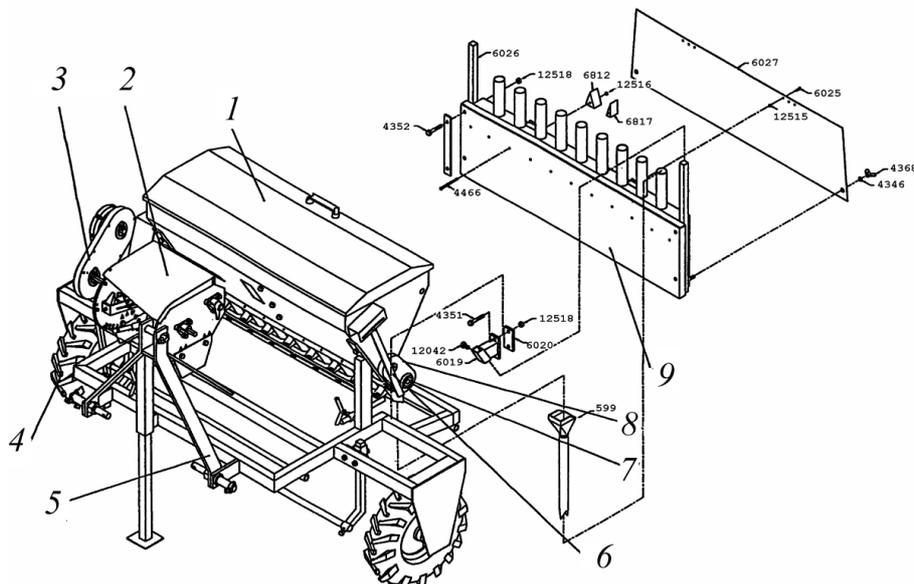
Общий вид сеялки «Egedal»: 1 – бункер для семян; 2 – многоступенчатый редуктор; 3 – цепная передача; 4 – правое приводное колесо; 5 – рама с навеской; 6 – рычаг регулировки размера щели высевающего аппарата; 7 – вал высевающих аппаратов; 8 – цепная передача привода ворошилки семян; 9 – приставка для сплошного посева семян
